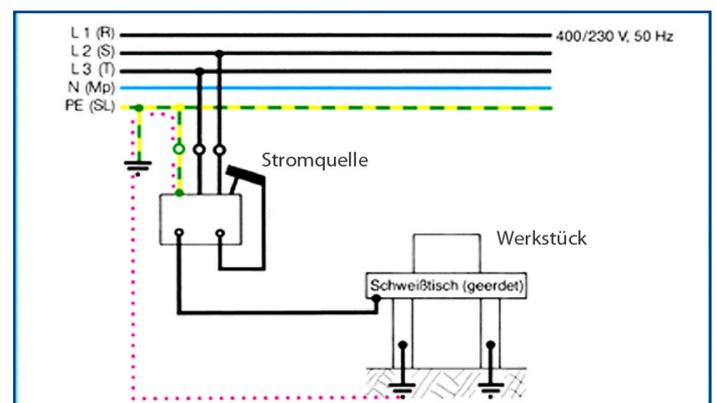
Beim nicht isolierten Ablegen des Stabelektrodenhalters auf die Schweissstromquelle kann deren Schutzleiter auch dann durchschmelzen, wenn das Werkstück oder der Schweißstisch auch ohne Elektrowerkzeug eine Erdverbindung besitzt. Der Weg des vagabundierenden Schweissstromes ist punktiert
